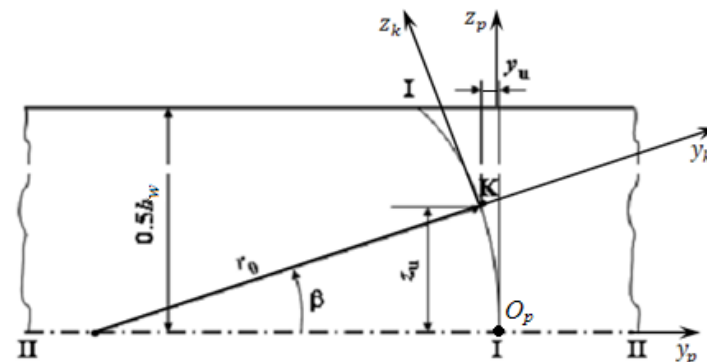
Зуб арочного полушеврона производящей рейки для шестерни с вогнутой рабочей стороной
